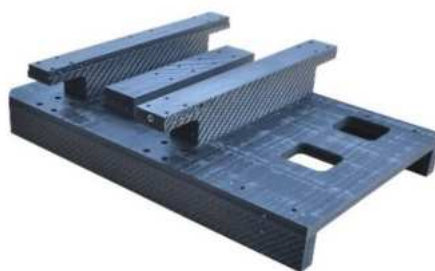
Sanie pentru m-u CNC din fibră de carbon [42]
